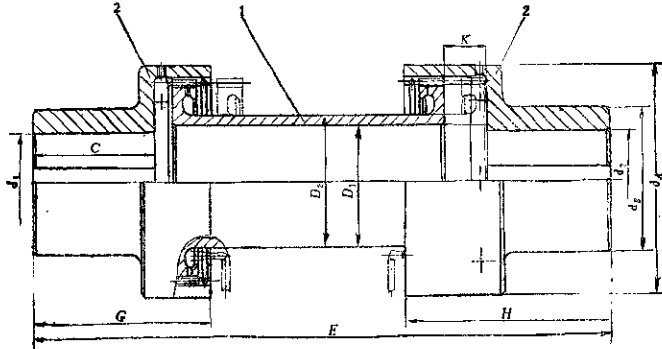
CL-H1型高速直齿齿轮联轴器
